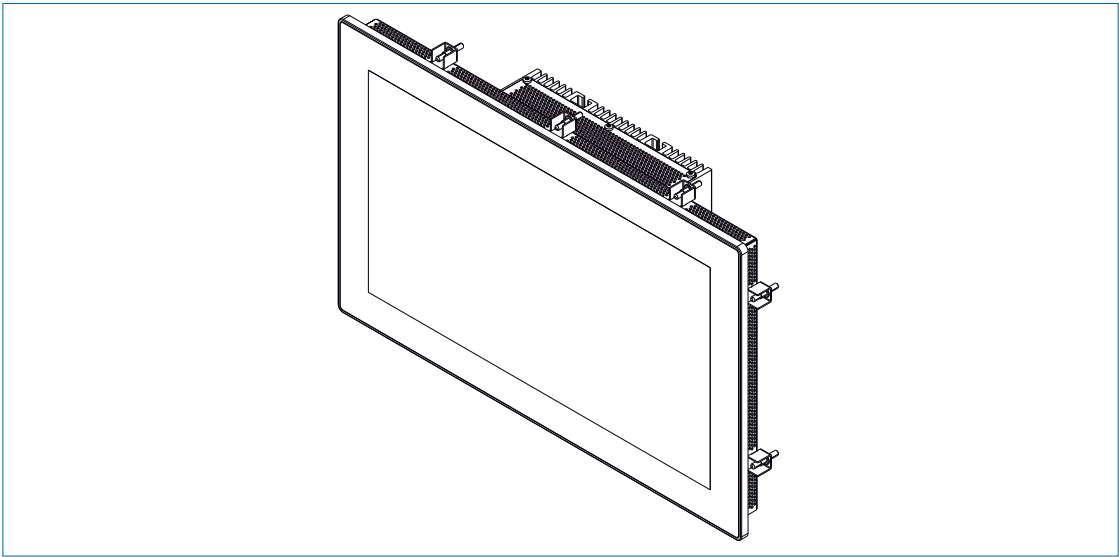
15,6“ Prime Panel Pico Einbau - Geräteansicht
